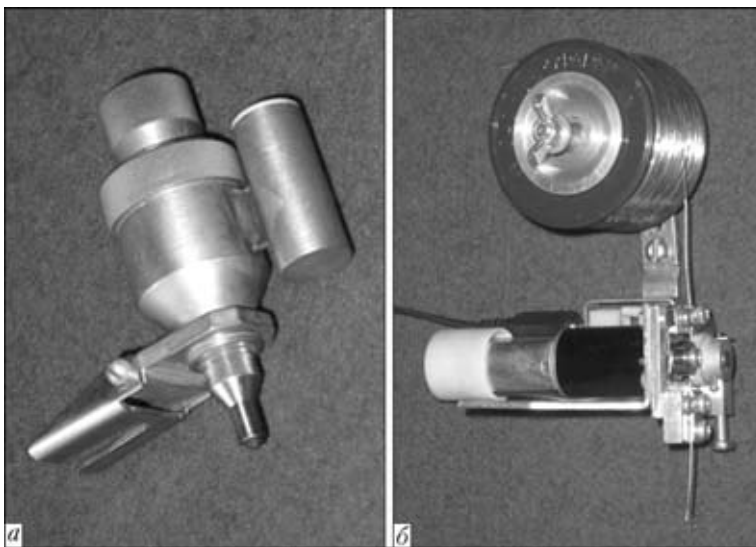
Внешний вид порошкового дозатора МПД-004 (а) и устройства для подачи проволоки МППН-04 (б)
